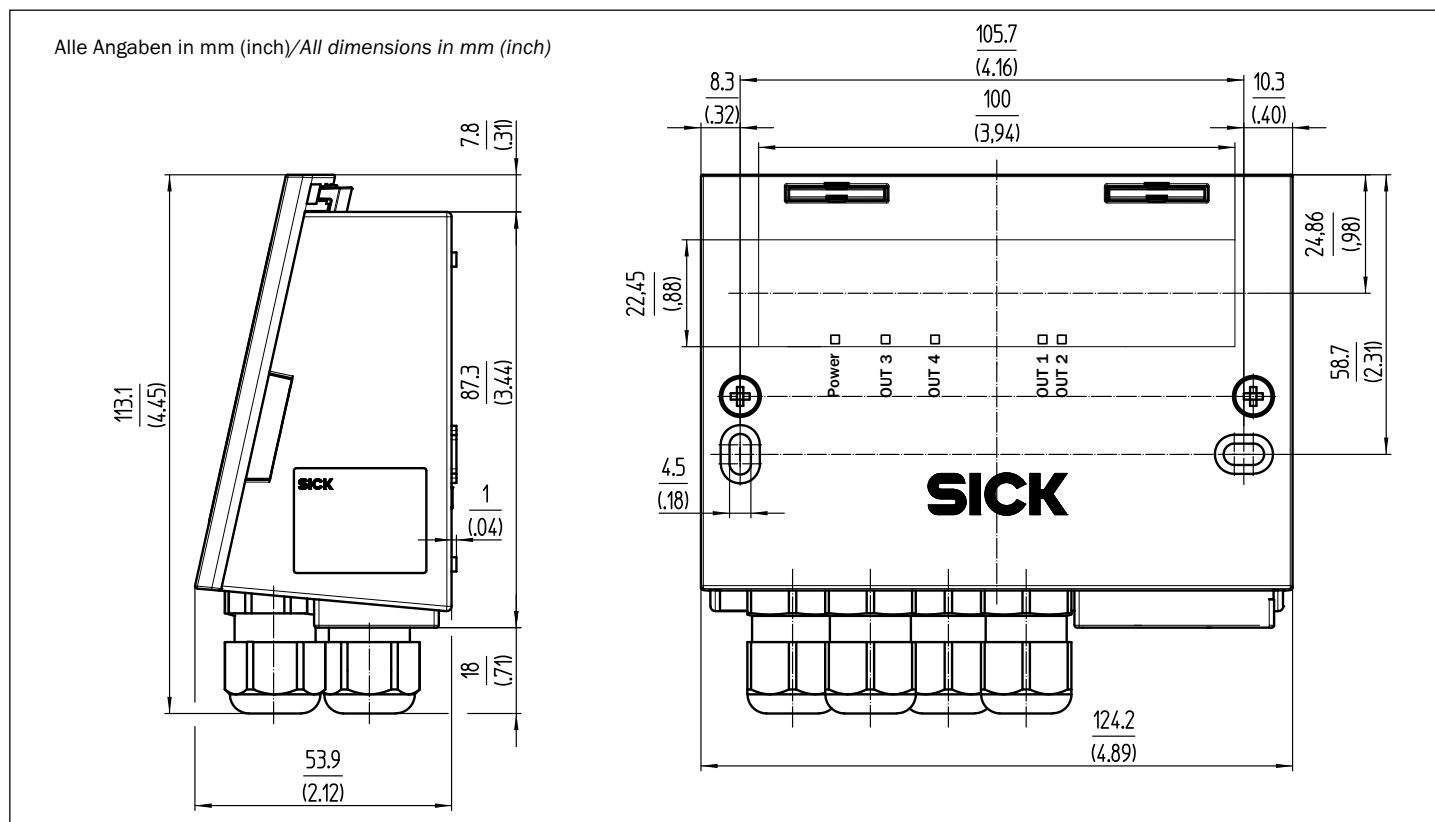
Abmessungen des CD730-001/ Fig. 1: Dimensions of the CDB730-001
